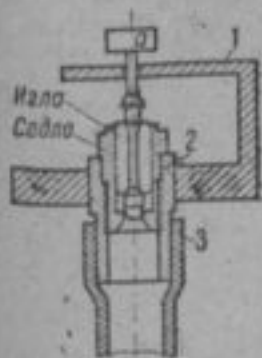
Проверка узла запорной иглы поплавковой камеры
